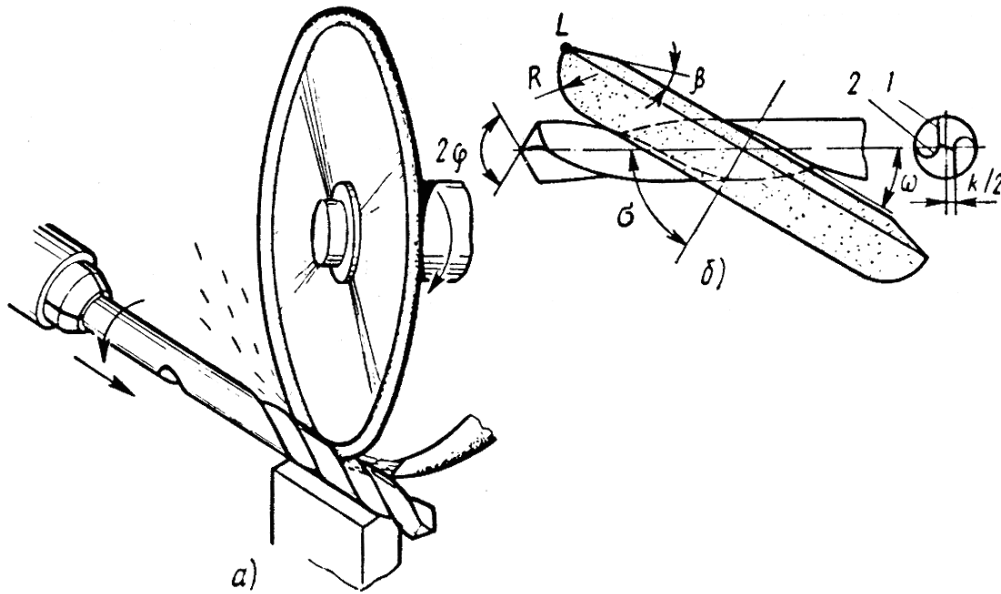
Расположение спирального сверла и абразивного инструмента при вышлифовке винтовых стружечных канавок:
